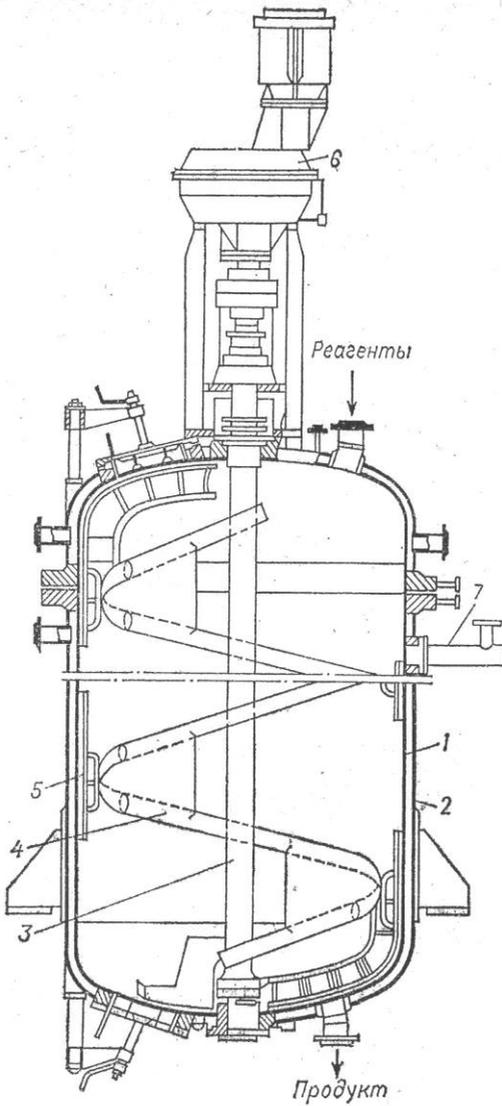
Конструкция реактора-полимеризатора скребкового типа: 1 - корпус; 2 - рубашка; 3 - вал ротора; 4 - ленточная мешалка; 5- скребок; 6 - мотор-редуктор
